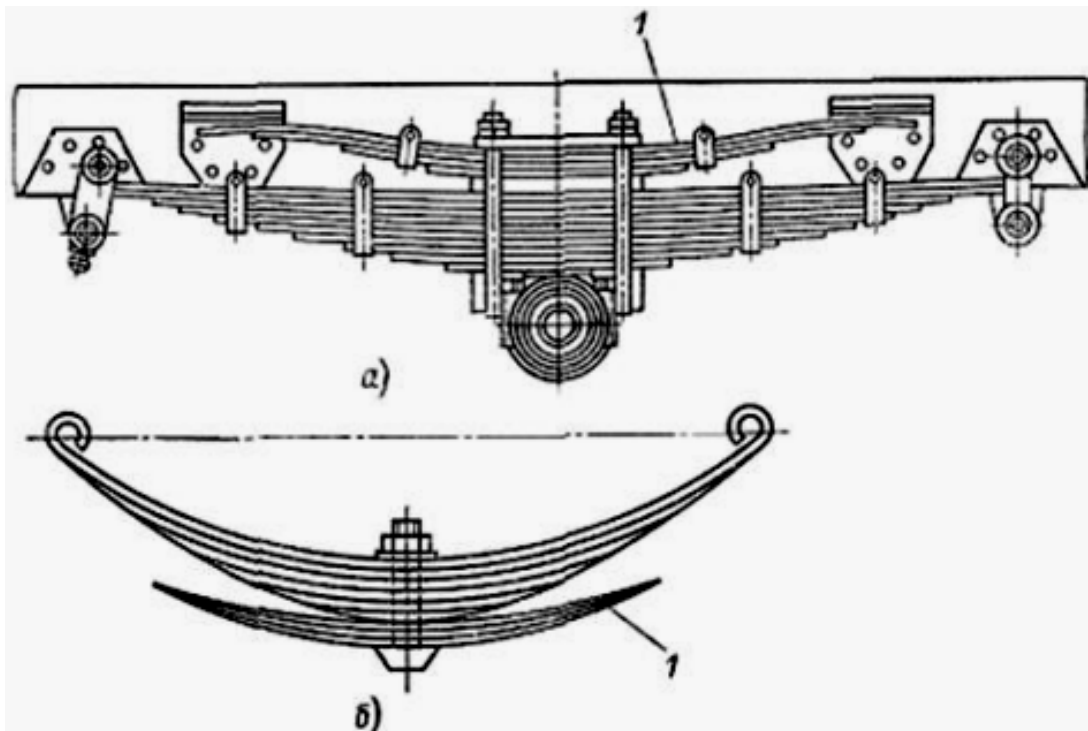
Подвеска с расположением подрессорника: а - сверху основной рессоры; б - снизу основной рессоры
